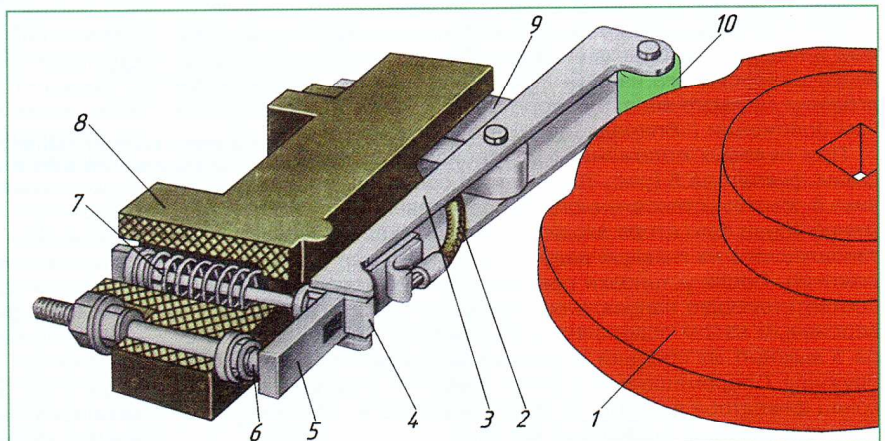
Контактный элемент контроллера типа КМЭ грузовых электровозов: 1 — кулачковая шайба; 2 — гибкий шунт; 3 — контактный рычаг; 4 — штифт; 5 — подвижный контакт; 6 — неподвижный контакт; 7 — пружина; 8 — изоляционная колодка; 9 — стойка; 10 — ролик
